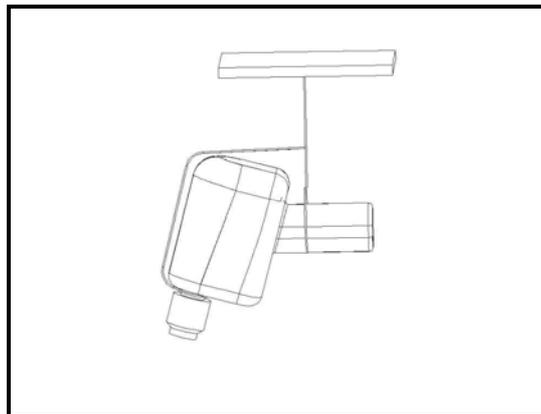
Aufhängevorrichtung für die Bohrmaschine
